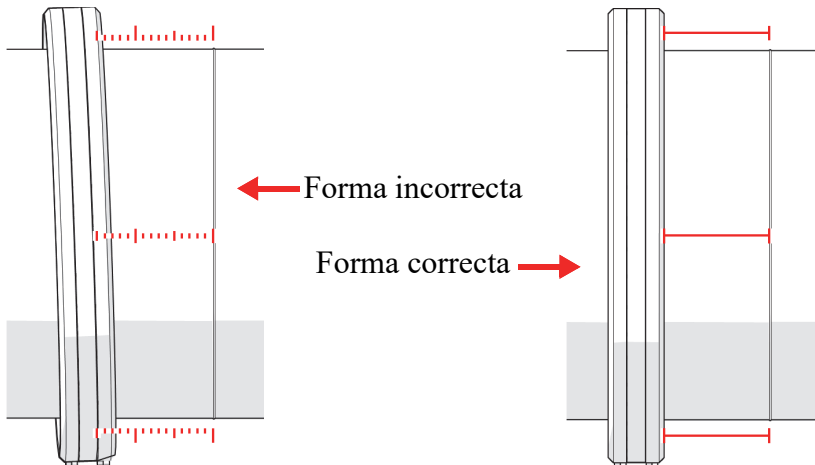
Alineación de la banda con respecto a la soldadura
